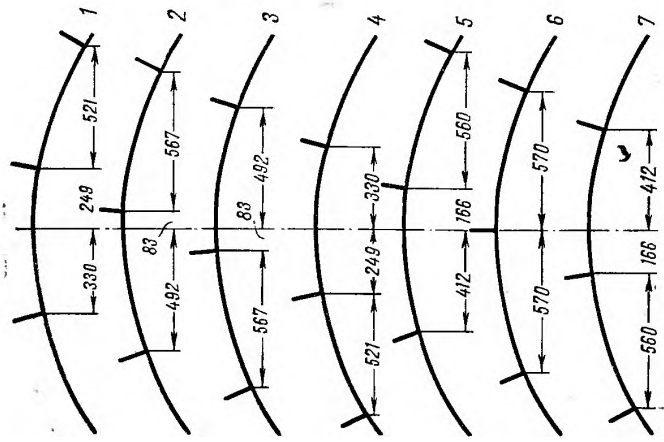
Схема расстановки зубьев на ковш экскаватора ЭТР231:
